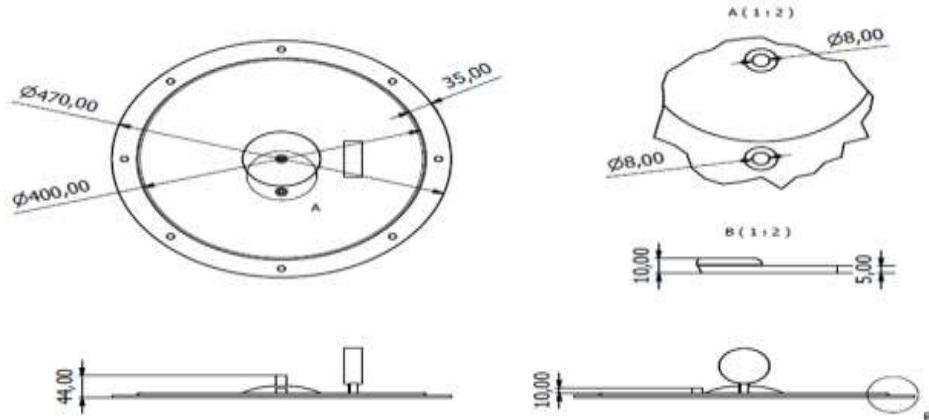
Tutup Tabung Reaktor 1 (3 dimensi)
